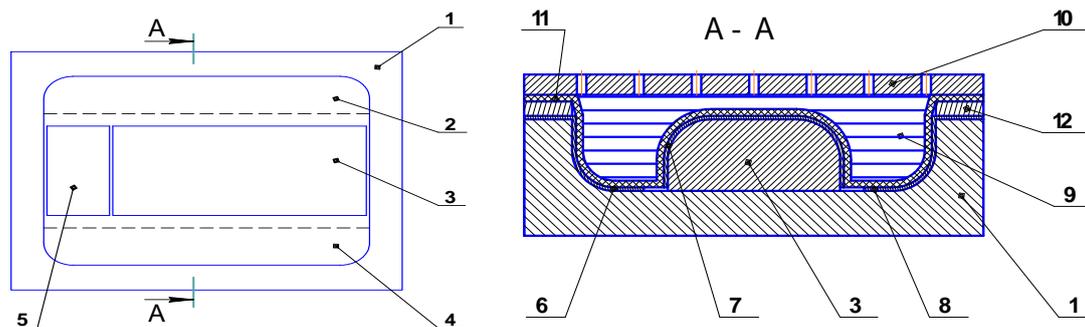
Оснастка индивидуально-универсальная: 1 – блок-матрица; 2, 4 – матричные поверхности для формовки листовой заготовки; 3 – оправка для формовки листовой заготовки; 5 – вспомогательный блок-вставка; 6, 7, 8 – листовые заготовки; 9 – рабочая полость; 10 – направляющая плита многоэлектродного разрядного блока; 11 – резиновая диафрагма; 12 – прижимная плита
